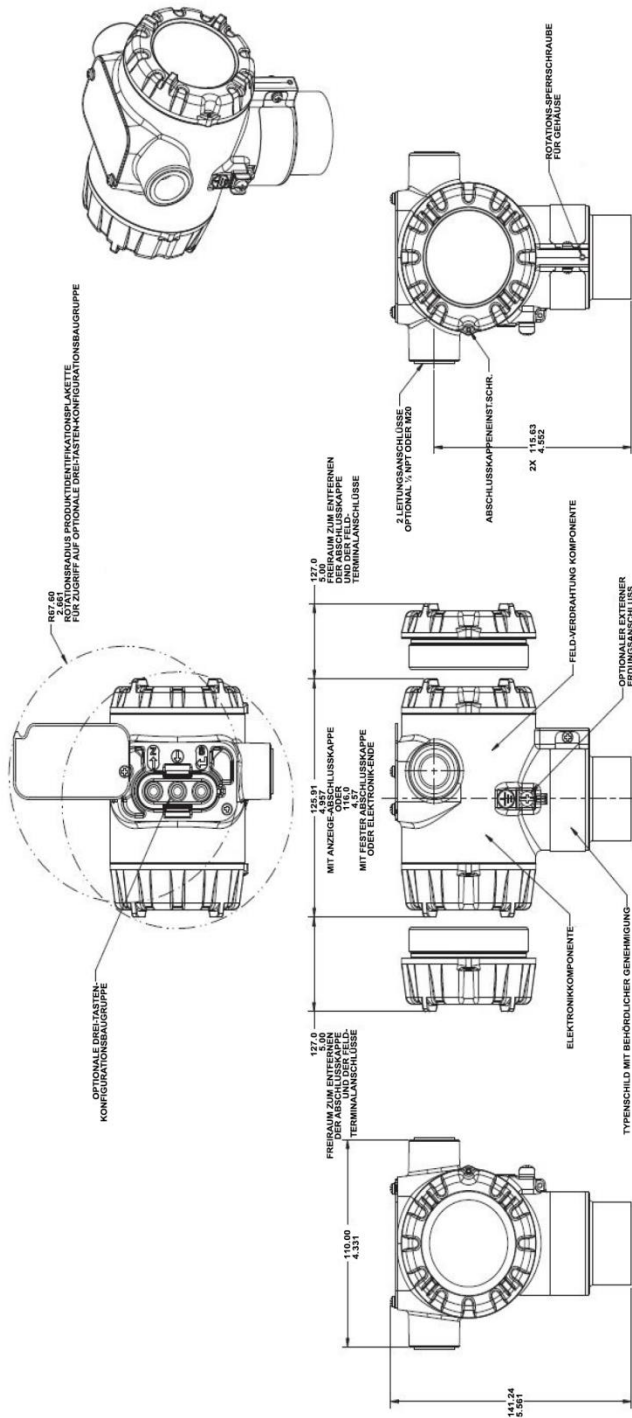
STT750 mit Adaptergehäuse - Abmessungen
